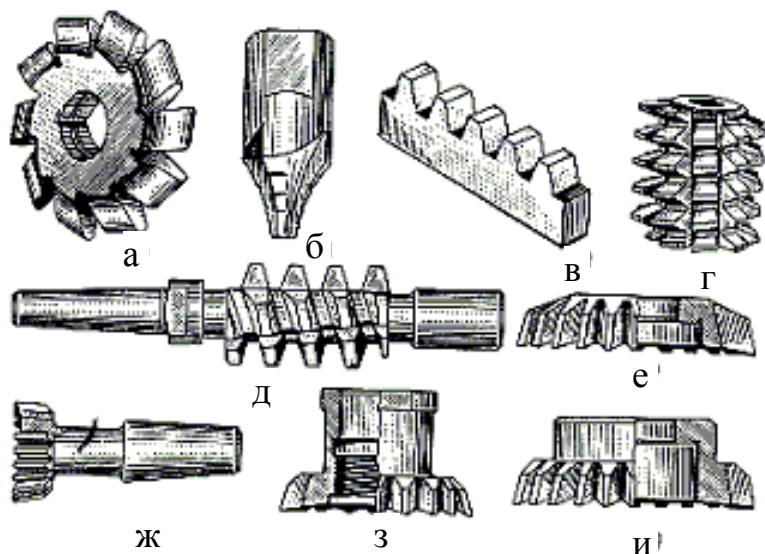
Ріжучий інструмент для зубонарізних робіт: а - модульна фреза; б – пальцева фреза; в – гребінка; г – черв'ячна насадна фреза; д – черв'ячна хвостова фреза; е – дисковий довб'як; ж – хвостовий довб'як; з – чашковий довб'як; и – втулковий довб'як.
